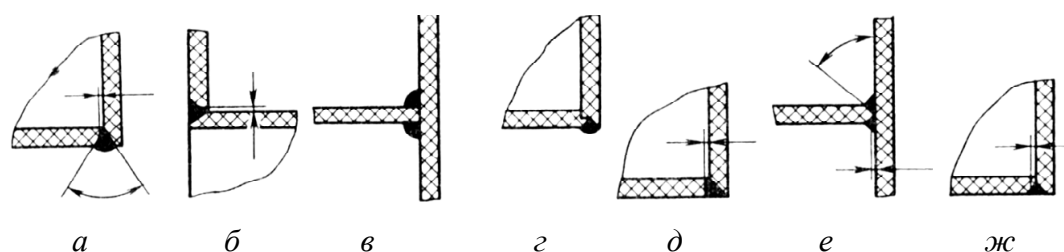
Примеры конструирования угловых и тавровых сварных соединений:
